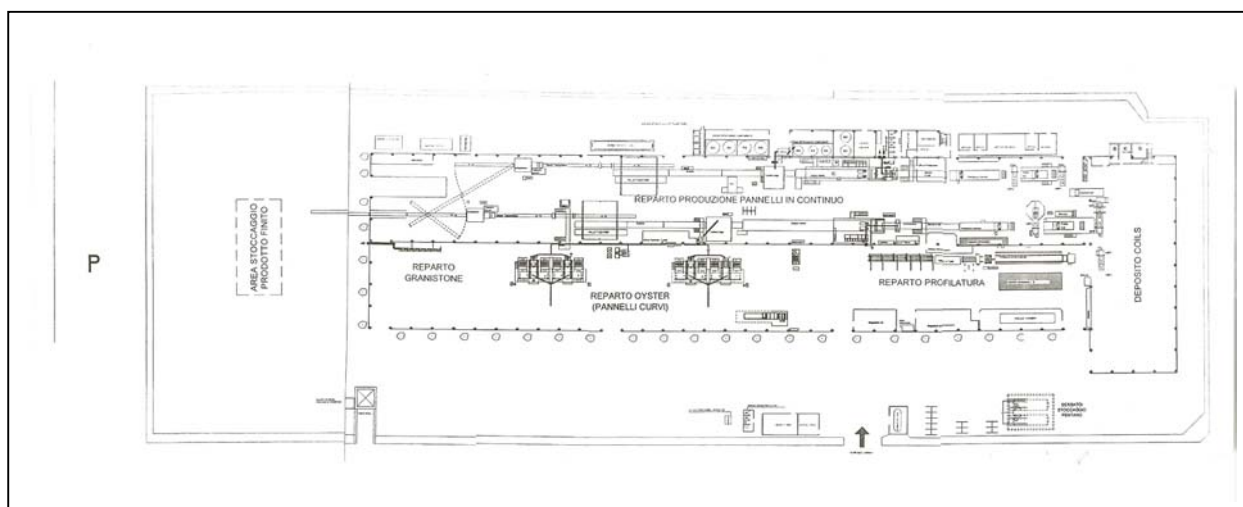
Planimetria schematica dello stabilimento SIS.CO. (fornita da SIS.CO. S.p.a.)
